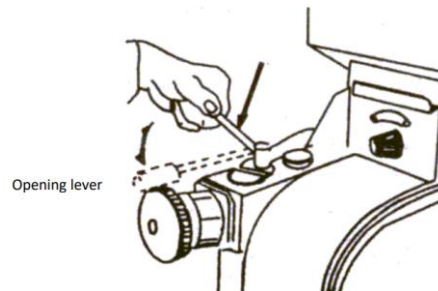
Feeding Shutter, Adjusting valve, dan Indicating Handle
